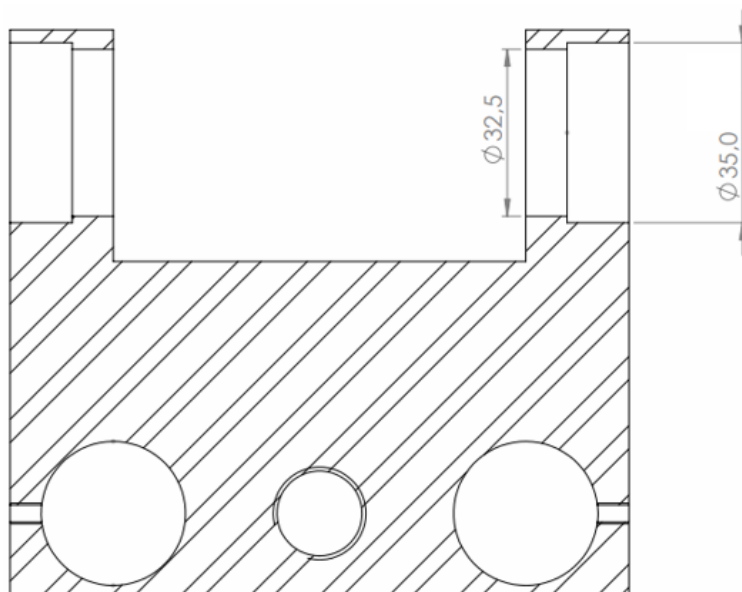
Dimensiones del alojamiento para la del rodamiento por ajuste
